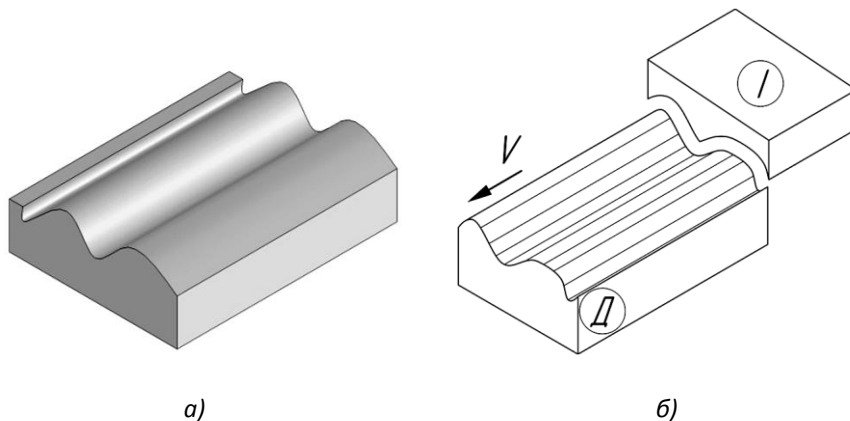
Оброблення фасонних циліндричних поверхонь при прямолінійно-поступальному русі: а — фасонна циліндрична поверхня; б — оброблення циліндричної поверхні
